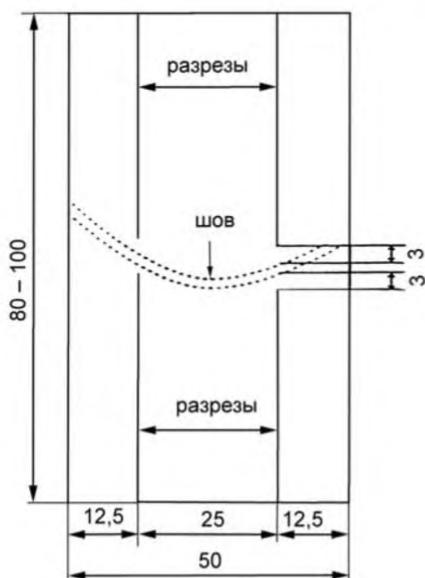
Образец для испытаний, вырезанный из обуви
